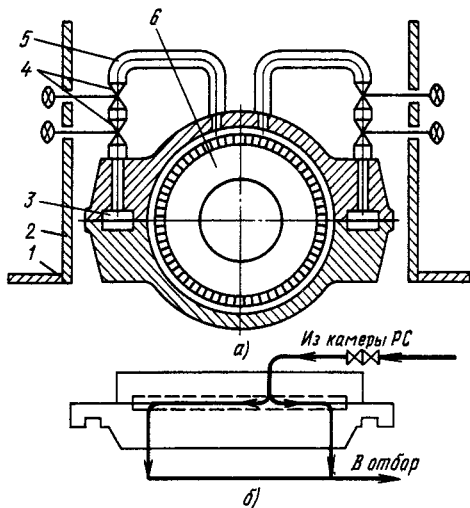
Новая система обогрева фланцев: а — поперечный разрез корпуса ЦВД по камере регулирующей ступени; б — схема потоков греющего пара; 1 — площадка обслуживания; 2 — обшивка турбины; 3 — обнизка; 4 — запорные вентили; 5 — трубопровод; 6 — камера регулирующей ступени
